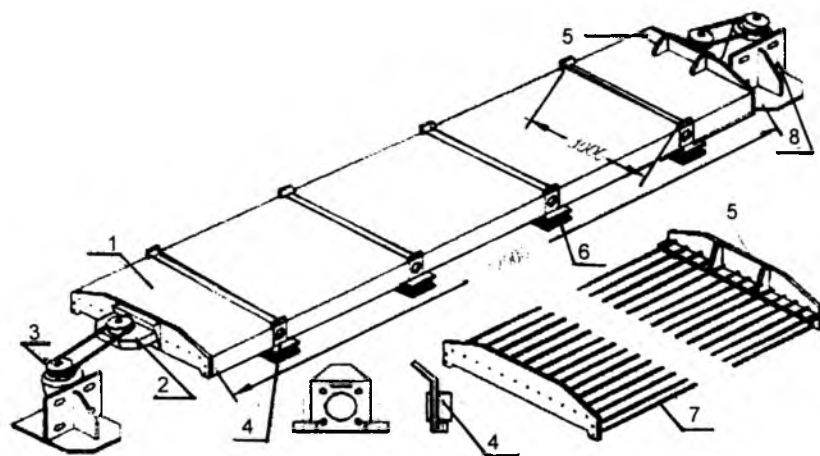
Схема виброплощадки ВПГ-3х12 ЖБ с железобетонной рамой (защитные кожухи над виброприводами не показаны)
